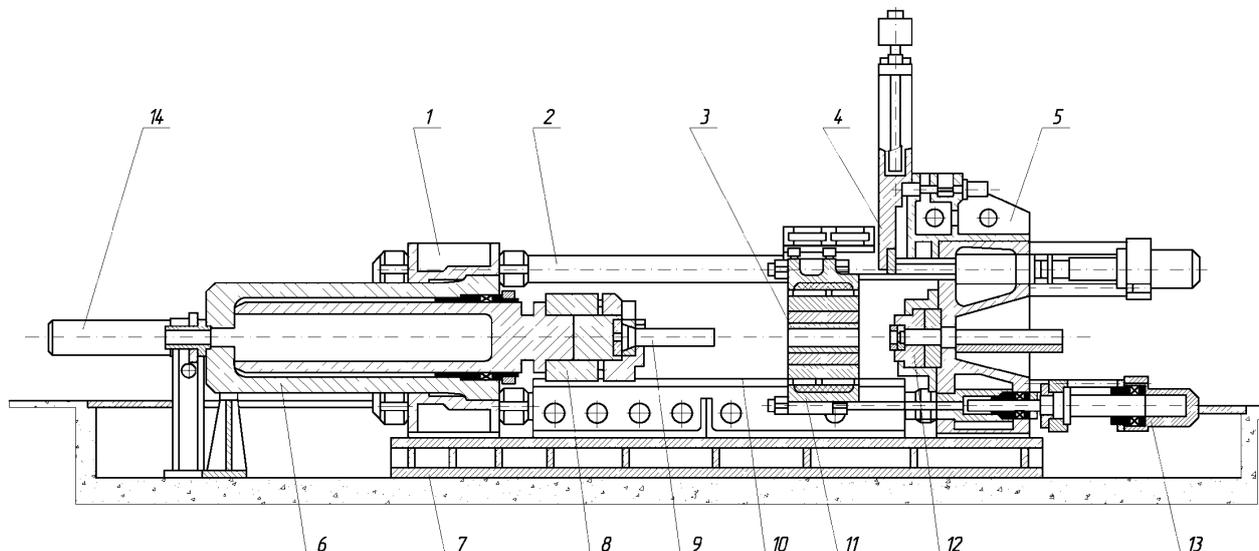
Схема типовой конструкции современного прутково – профильного горизонтального гидравлического пресса.
